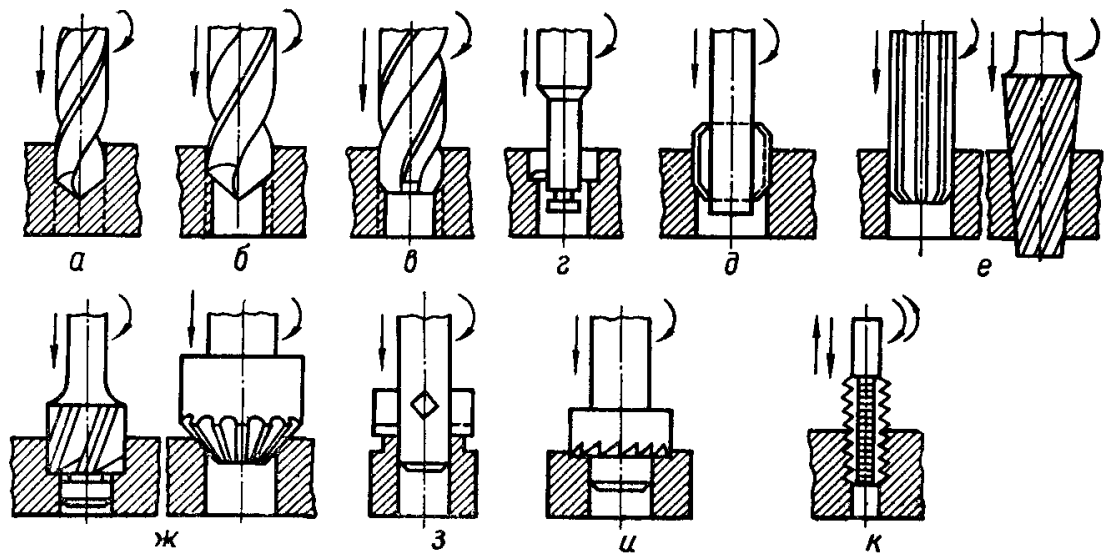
Схеми видів обробки на свердильних верстатах
